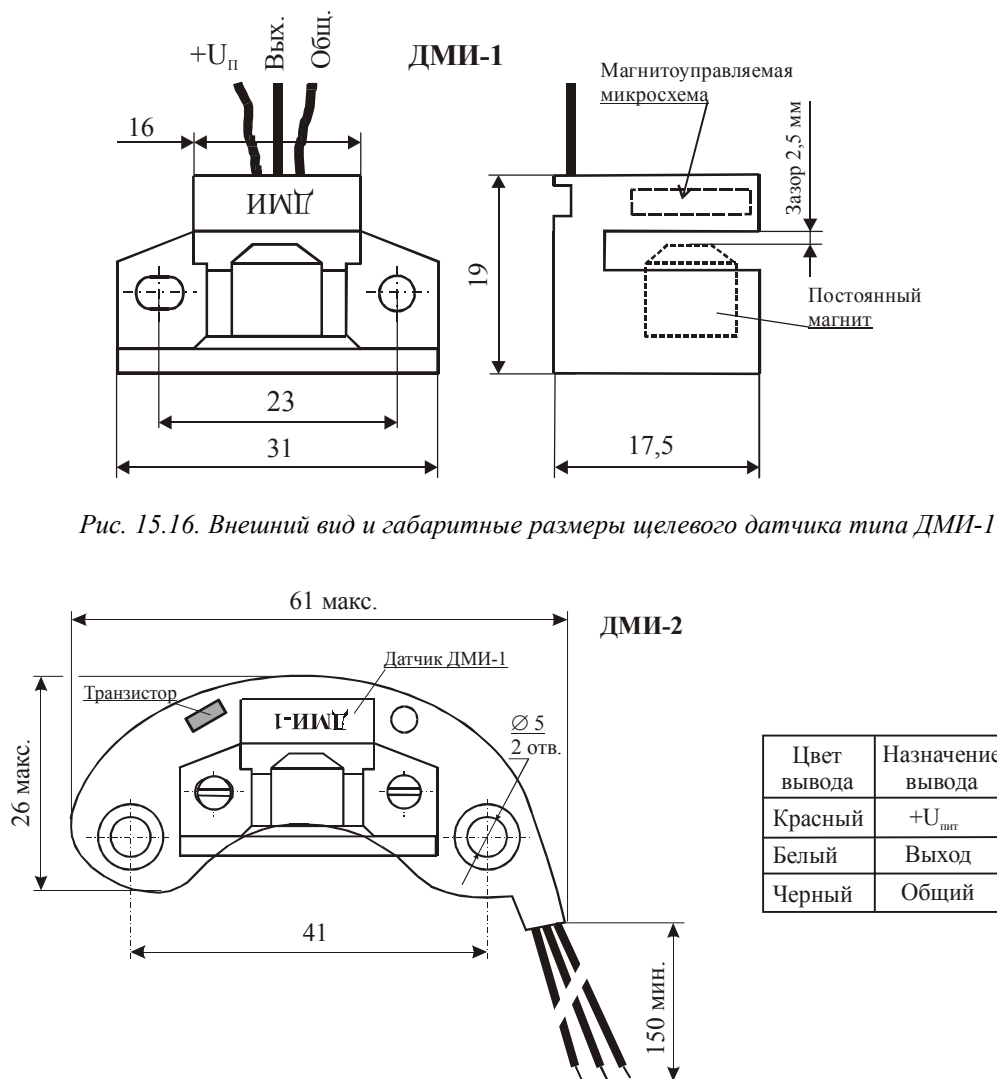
Внешний вид и габаритные размеры целевого датчика типа ДМИ-1
